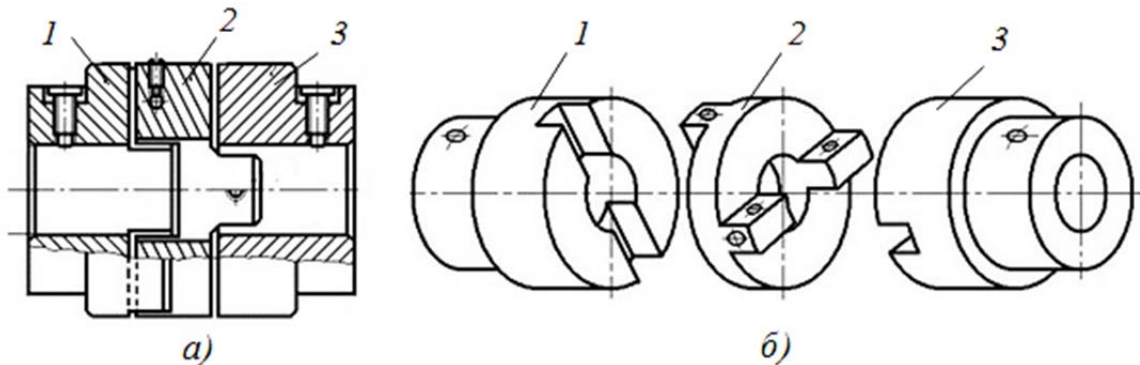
Кулачкова-дیسкова муфта: розріз(а), загальний вигляд деталей(б); 1,3 – напівмуфти; 2 – диск.
